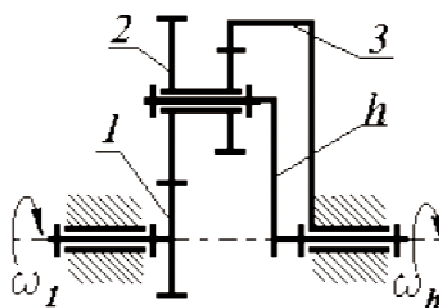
Схема двохрядного планетарного механізму з одним внутрішнім зачепленням: 1 – сонячна шестірня; 2 – сателіт; 3 – коронна шестірня;
